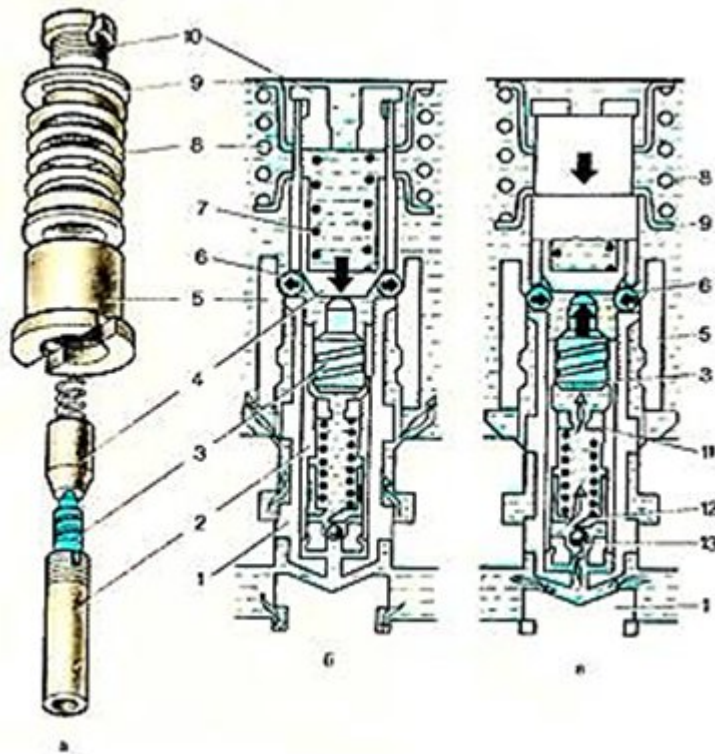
Принцип дії фіксувального пристрою і механізму повертання золотника
